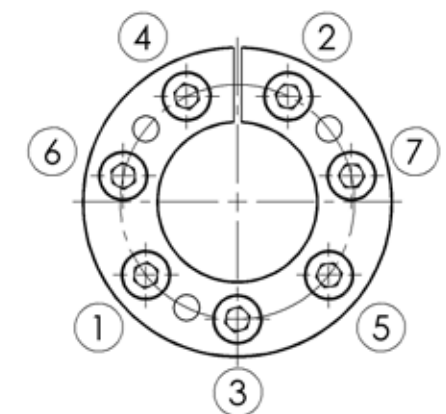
Sequenz Aufschraubung Schrauben auf Verbinder Zahnräder.
